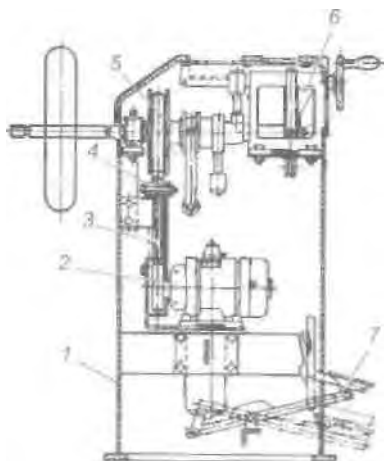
Балансировочный станок для колес легковых автомобилей: / — корпус; 2 — электродвигатель; 3 — ременная передача; 4 — тормозное устройство; 5 — балансировочный механизм; б — резонансный индикатор; 7 — педаль
